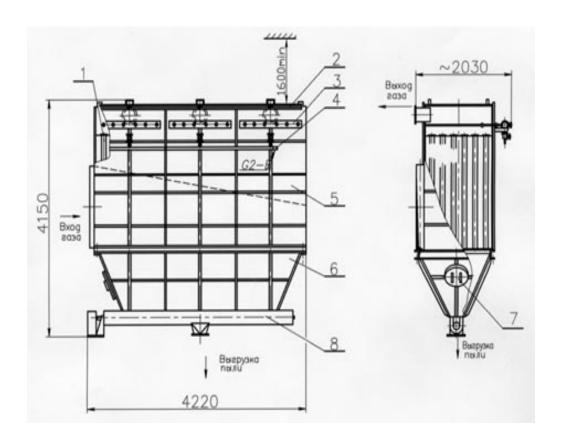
Рукавный фильтр ФРИ-90-02-Щ со щелевым бункером: 1 – рукав; 2 – крышка; 3 – клапанная секция; 4 – коллектор продувочного газа; 5 – корпус; 6 – бункер; 7 – люк; 8 – транспортер
